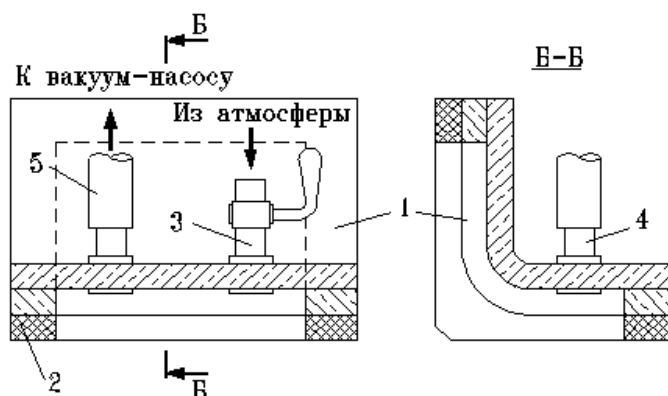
Вакуум-камера угловая для испытания герметичности сварных швов: 1 – корпус из оргстекла; 2 – губчатая резина; 3 – кран; 4 – патрубок; 5 – шланг
